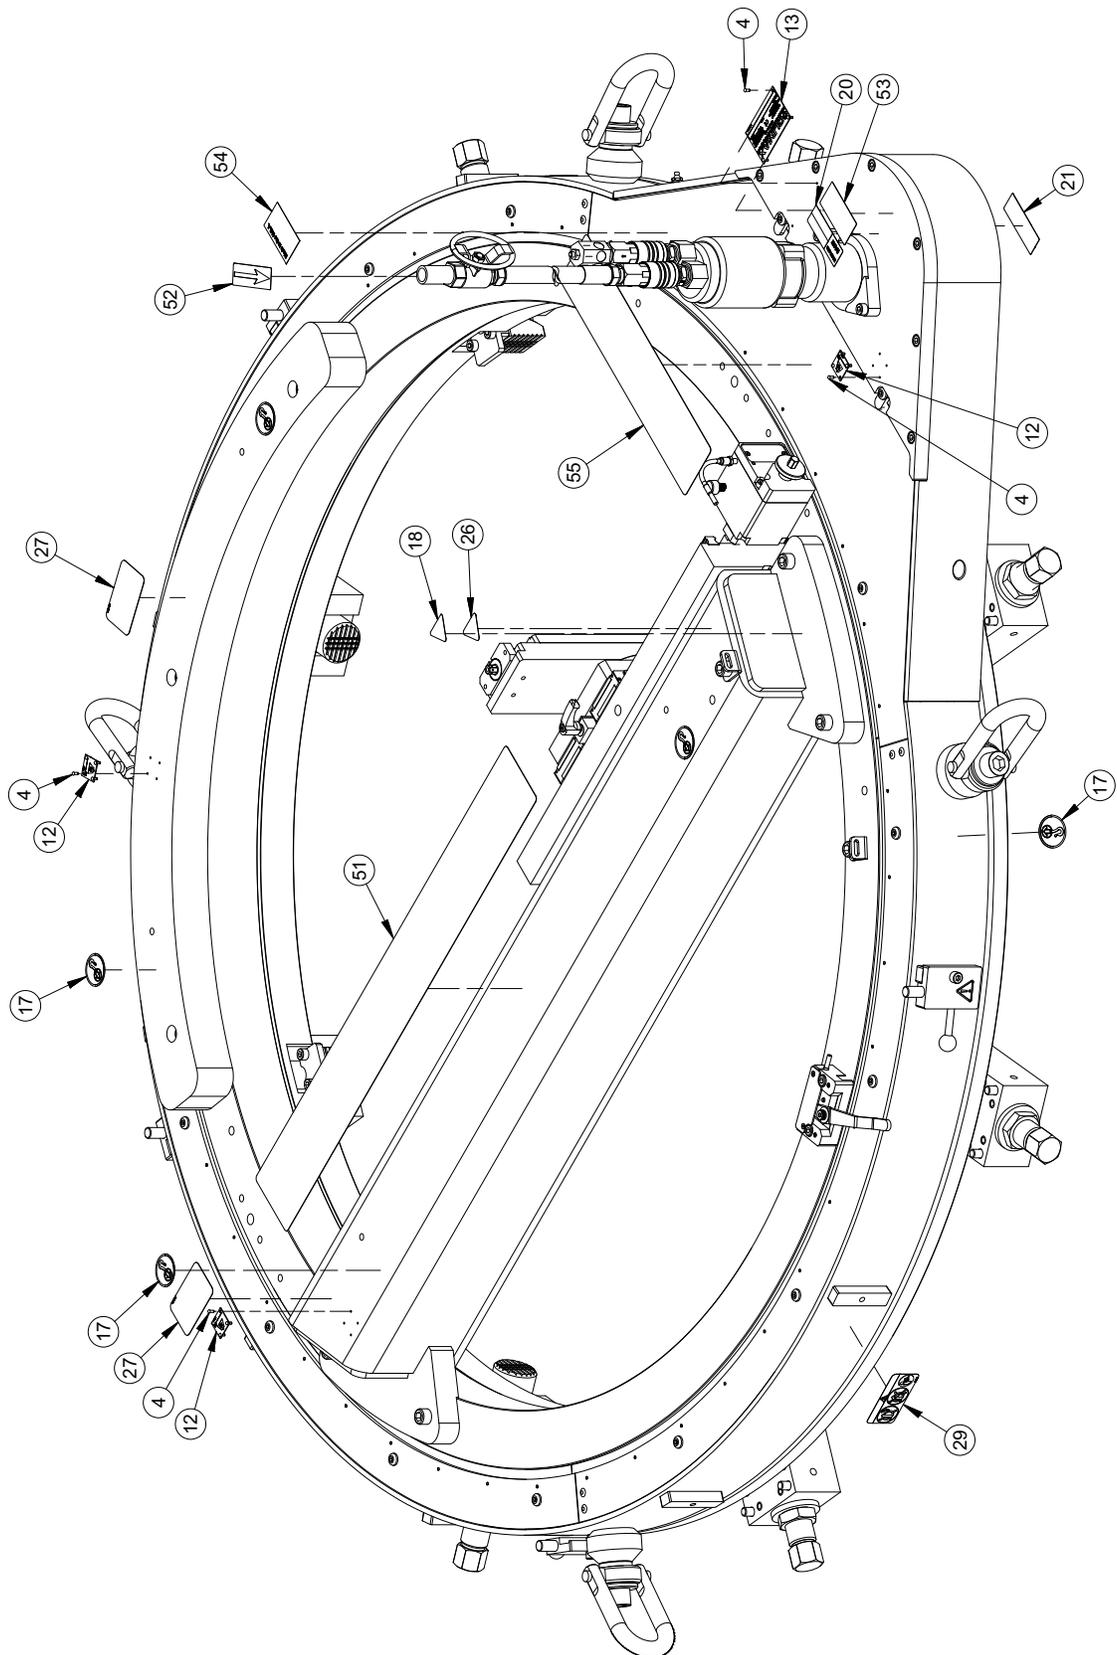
ENSEMBLE DES ÉTIQUETTES DE LA MACHINE ODF50 SPEED FACER (RÉF. 86980)
